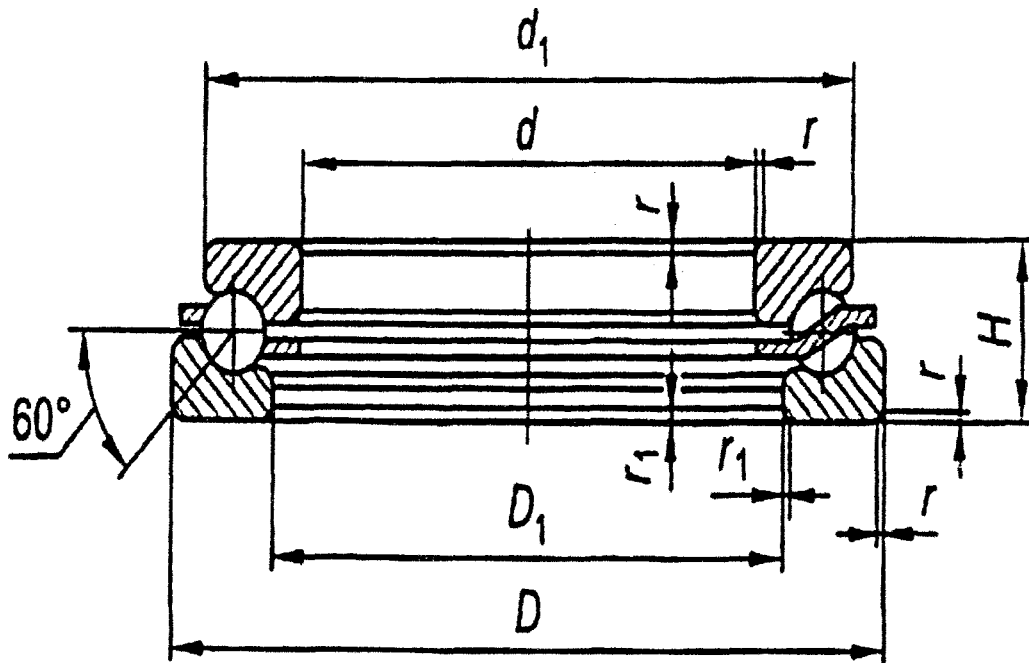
Подшипник шариковый упорно-радиальный одинарный исполнения 168 000
